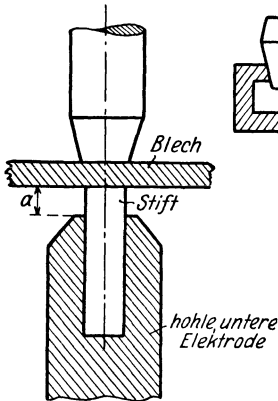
Elektroden für Zapfenschweißung.
